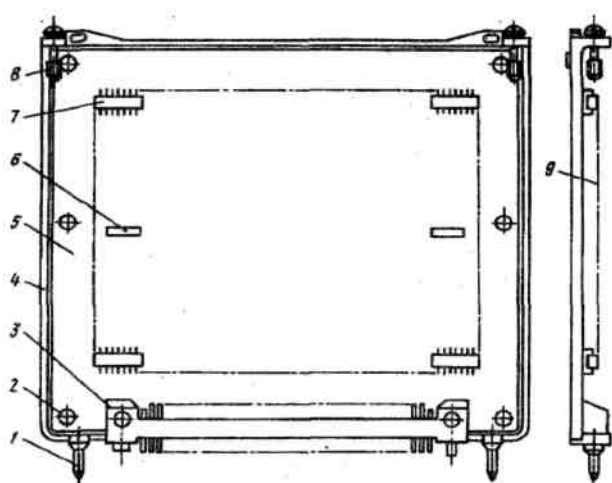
Конструкция ФЯ блока разъемного типа с разъемным соединителем типа ГРПМ: 1 – штырь-ловитель; 2 – развальцованная заклепка; 3 – вилка соединителя ГРПМ; 4 – обечайка; 5 – печатная плата; 6 – навесные ЭРЭ; 7 – корпусированная ИС; 8 – невыпадающий винт; 9 – зона установки схемных элементов
